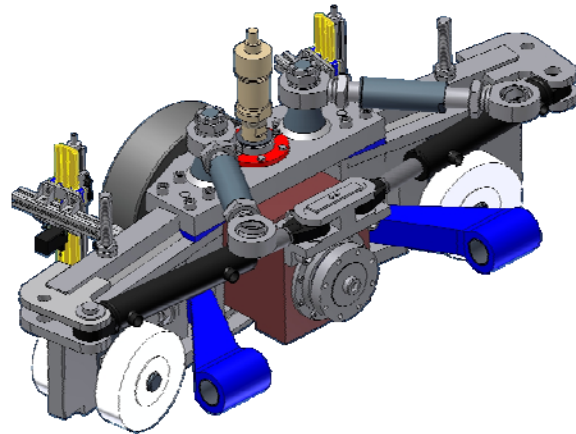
Radaufhängung mit Hydraulikzylindern, Unterlenkern (blau) und Oberlenkern
